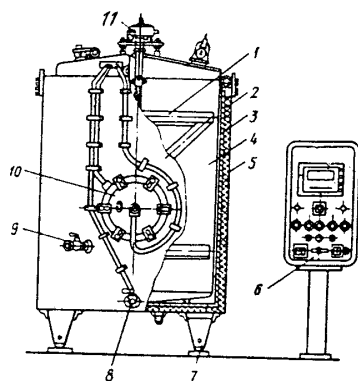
Резервуар для виготовлення кисломолочних продуктів: 1 – мішалка; 2 – теплоізоляція, 3 – теплообмінна сорочка; 4 – внутрішній корпус; 5 – зовнішній корпус; 6 – пульт керування; 7 – ніжки; 8 – патрубок заповнення-опорожнення; 9 – пробовідбірний кран; 10 – люк; 11 – привод мішалки
